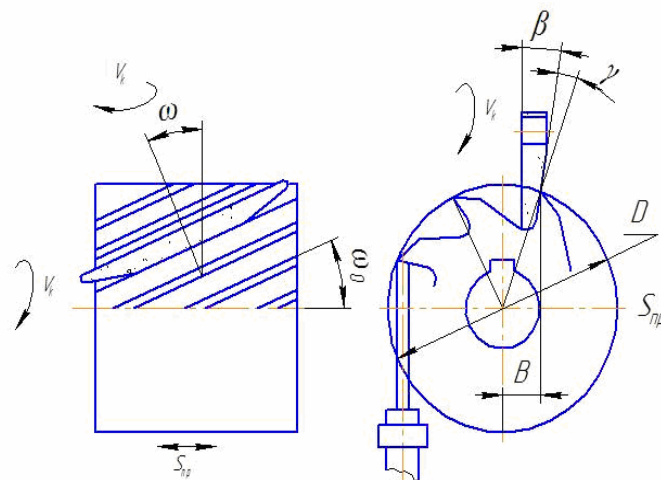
Схема заточування циліндричної фрези по передній поверхні
